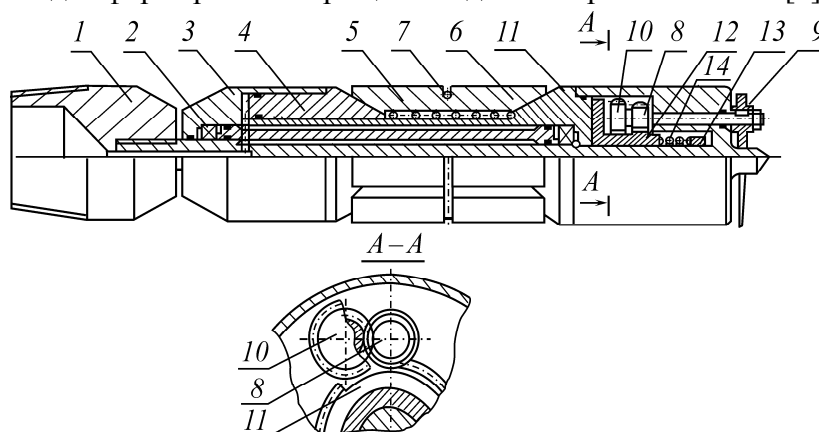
Фрикционный щелеобразователь с зубчатой передачей: 1 — корпус; 2 — подшипник; 3 — цилиндр; 4 — поршень; 5 — возвратная пружина; 6 — кулачок; 7 — пружинное кольцо; 8 — ось-шестерня; 9 — режущий орган; 10 — двойная шестерня; 11 — двухсекционное зубчатое колесо; 12 — тормозная втулка; 13 — гайка; 14 — пружина
